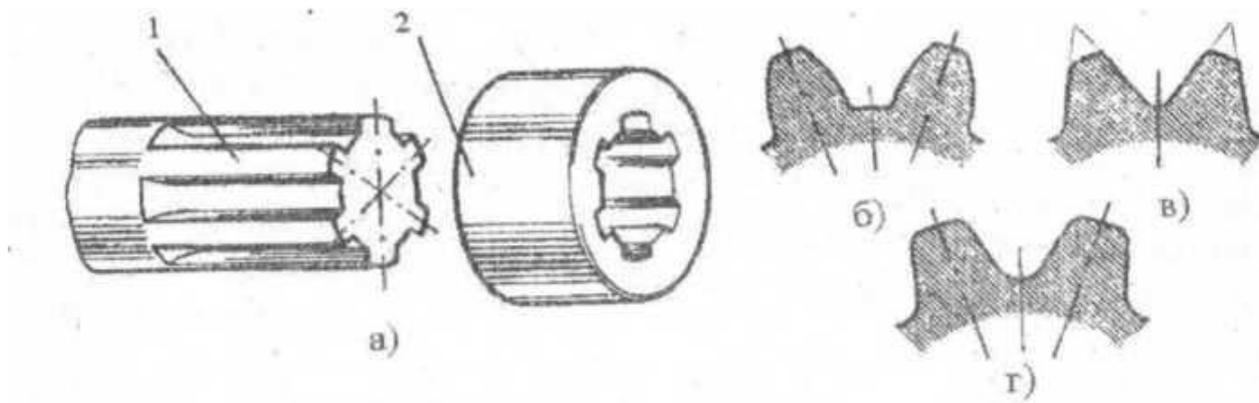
Разновидности шлицевых соединений: а – прямобочное;
